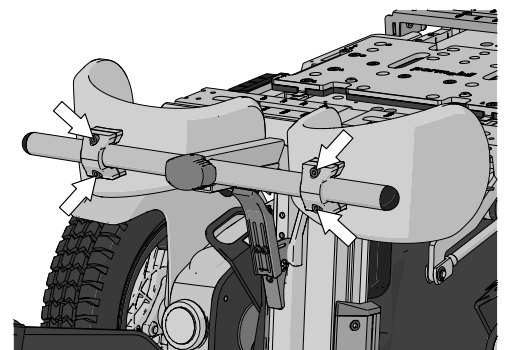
Auf jeder Halterung sind zwei Schrauben.
